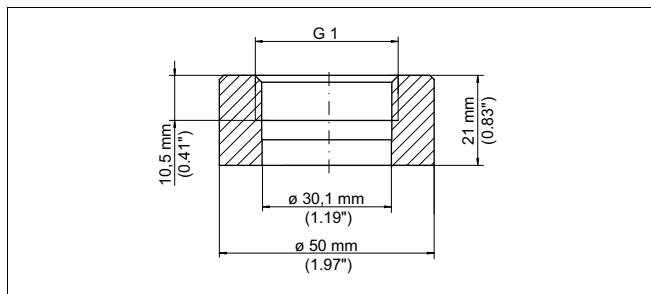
Размеры приварного штуцера G1 B по ISO 228-1
